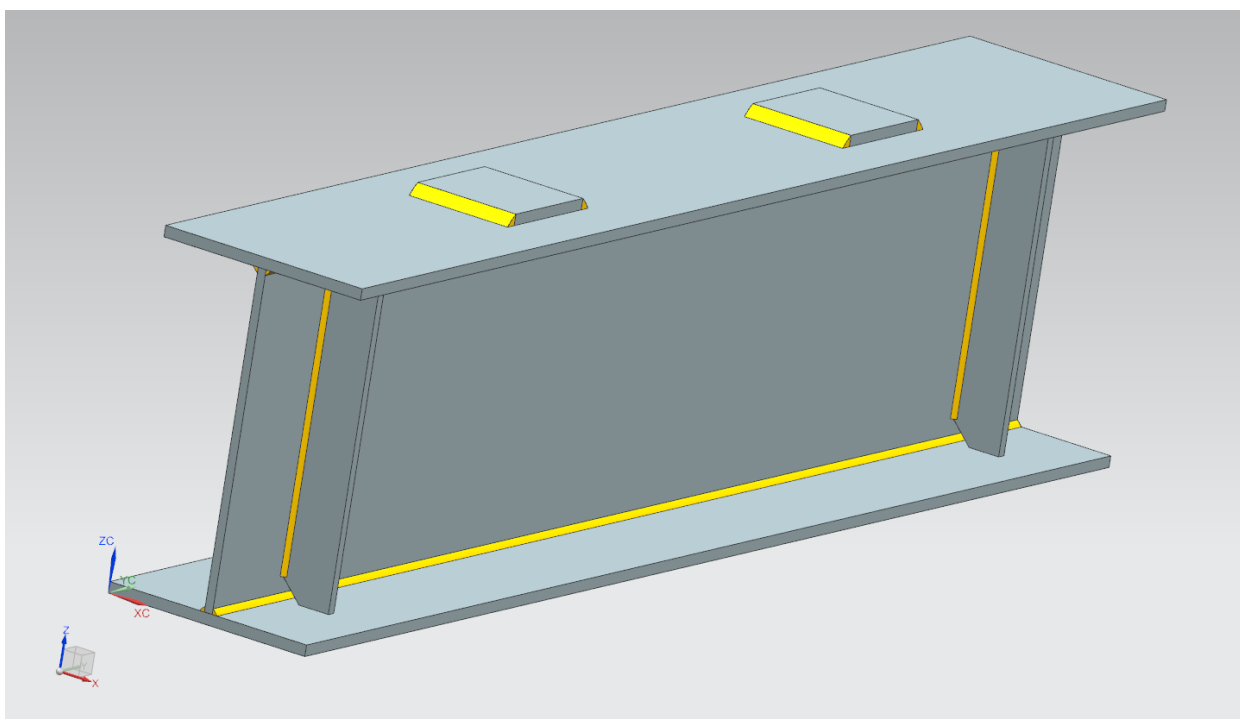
Модель сварной балки со сварными соединениями
